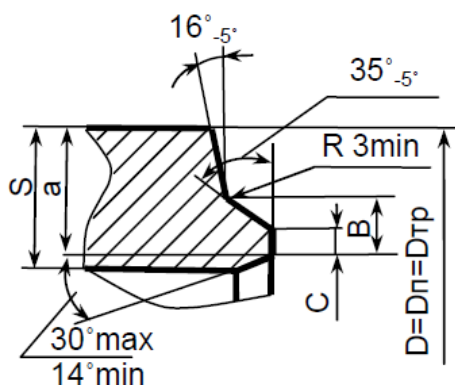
Геометрические параметры заводской разделки кромок торцов труб для сборки под сварку
